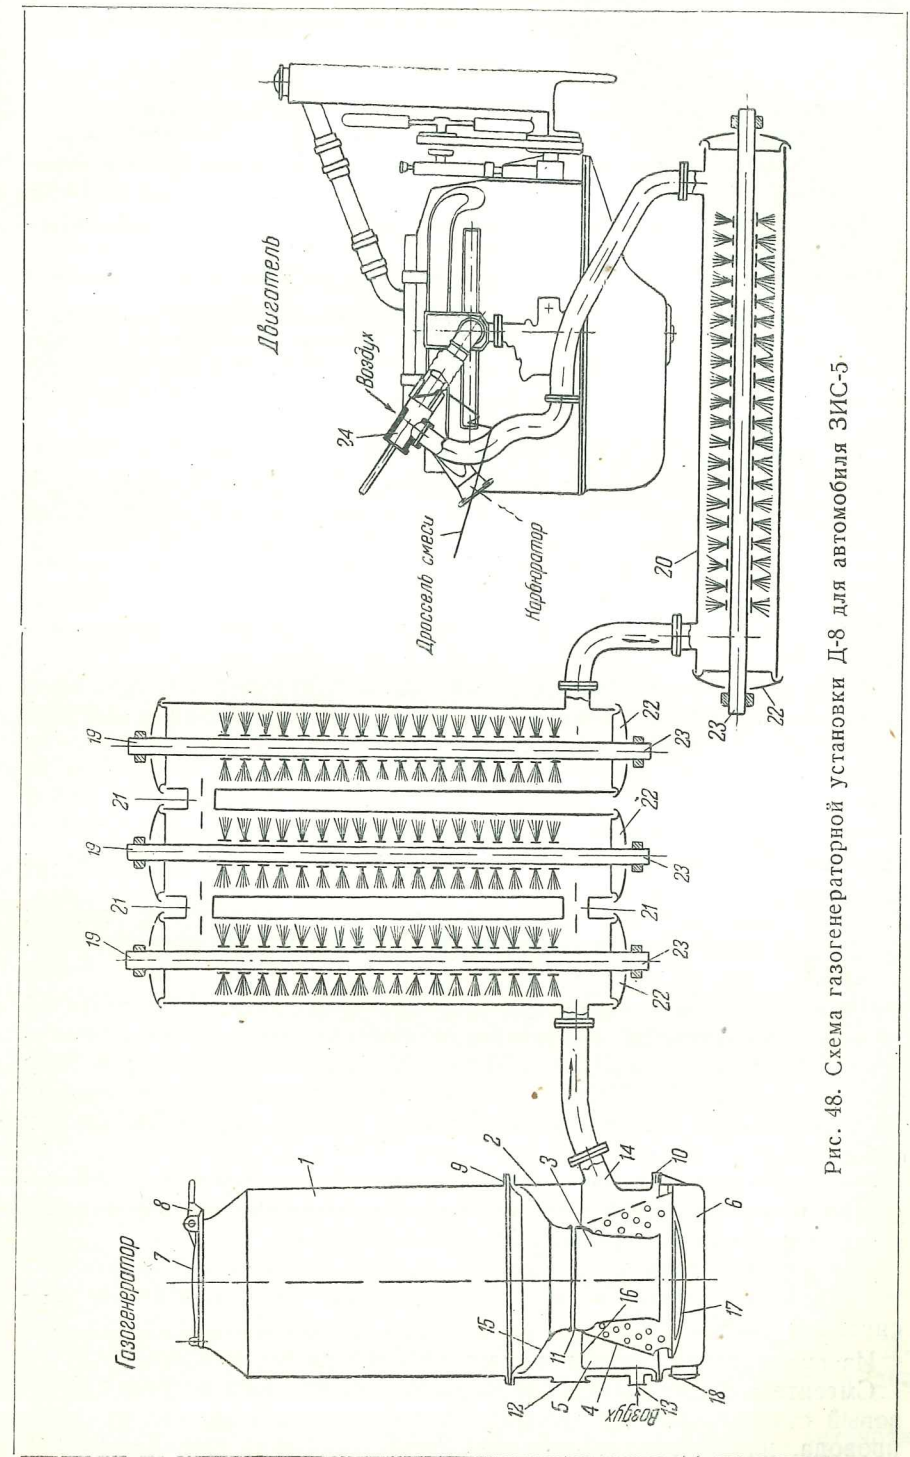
Схема газогенераторной установки Д-8 для автомобиля ЗИС-5.
